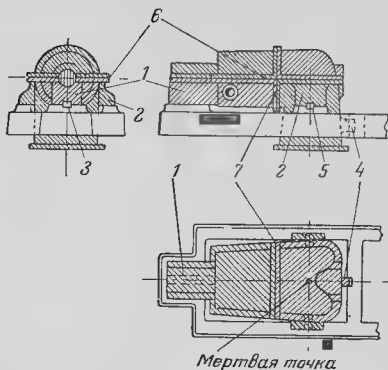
Схема крепления корпуса на фундаментной плите.
